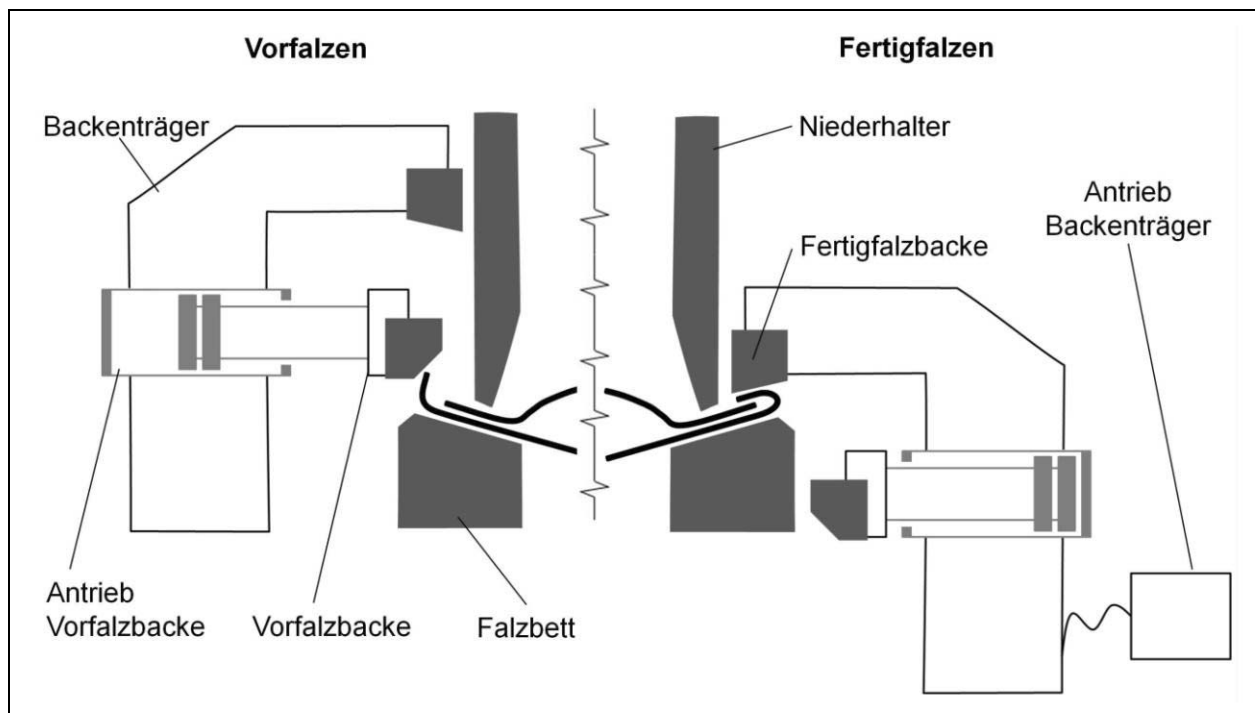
Schematische Darstellung des Aufbaus einer Maschinenfalzvorrichtung, hier für eine Anlage mit festem Falzbett
